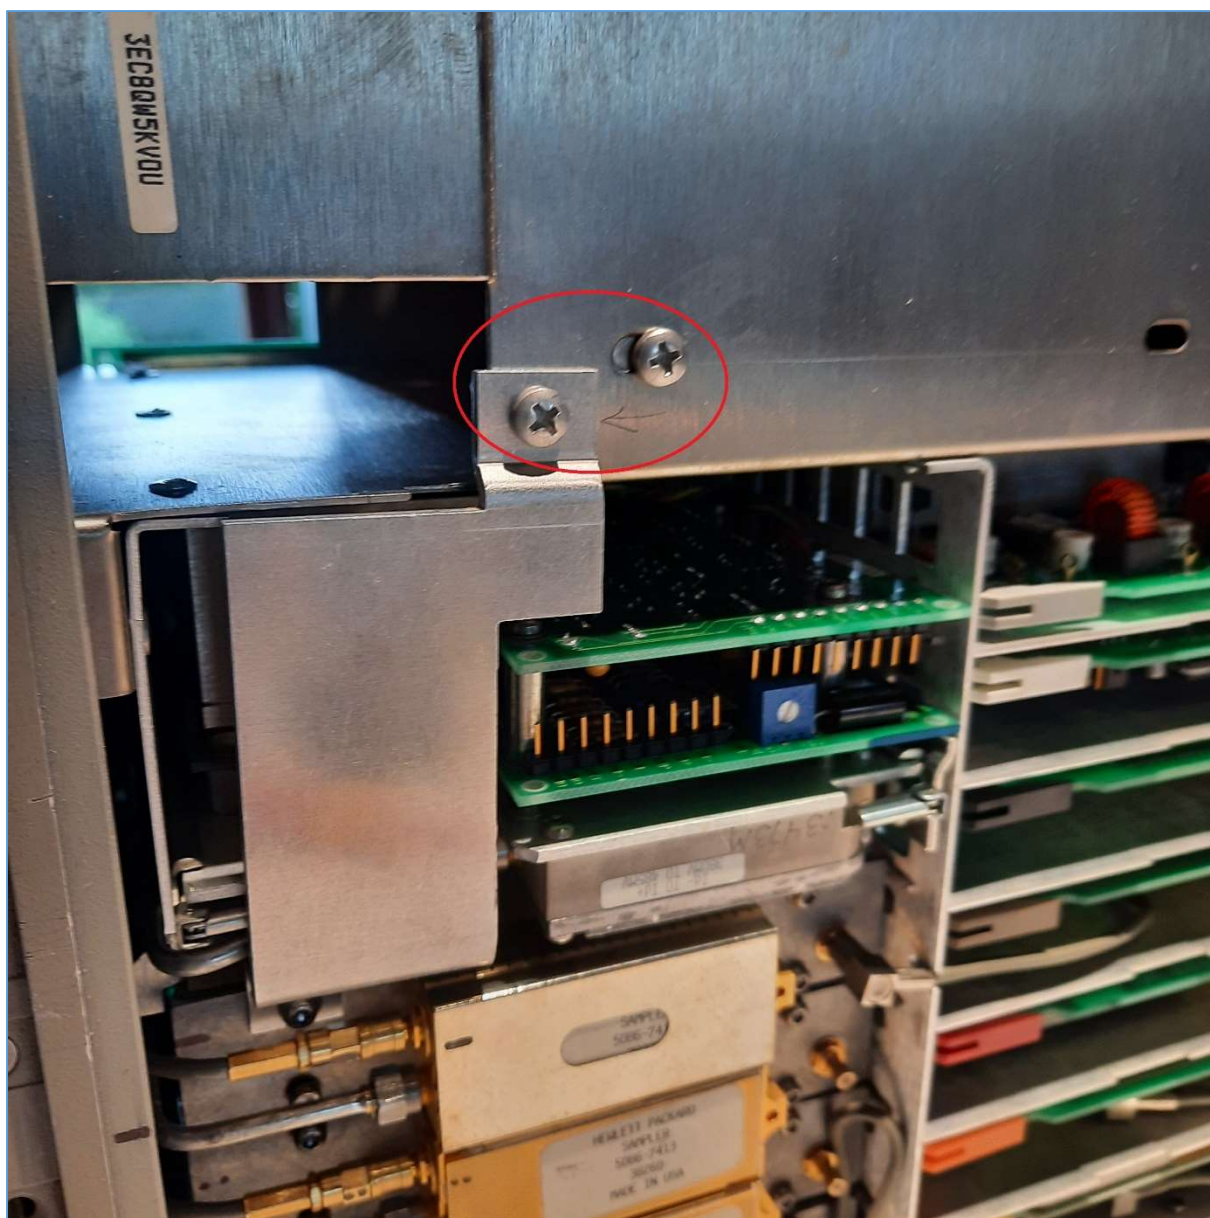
Fixation de la patte d'arrimage du bloc YTO du VNA. Photo : ON4IJ.
